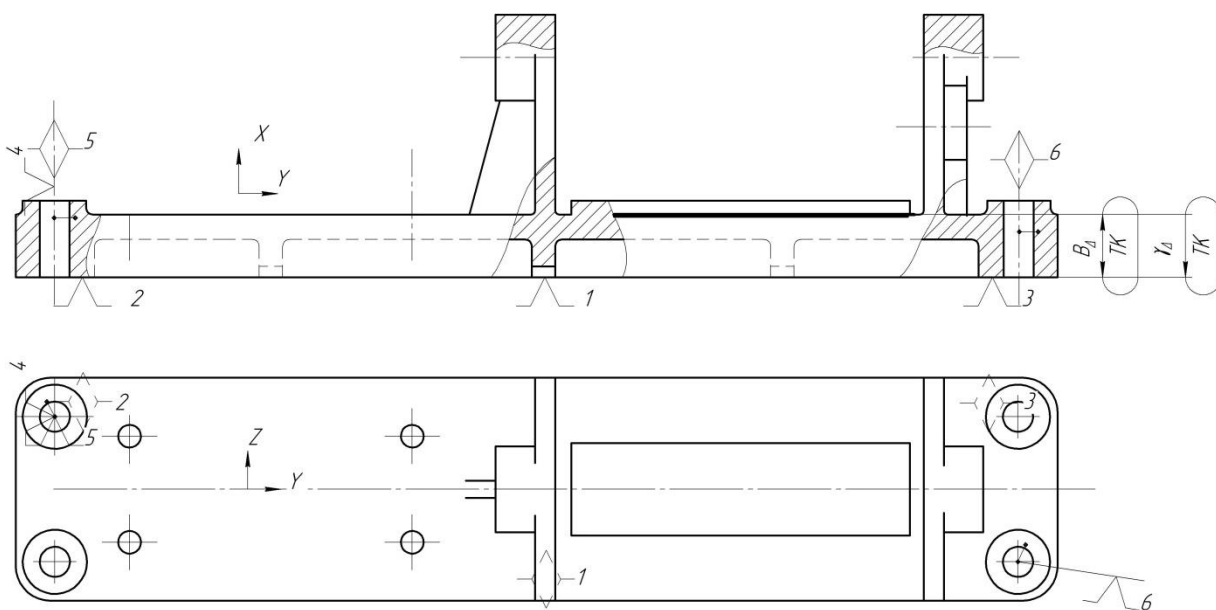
Перший варіант базування станини при обробці поверхні під корпус
